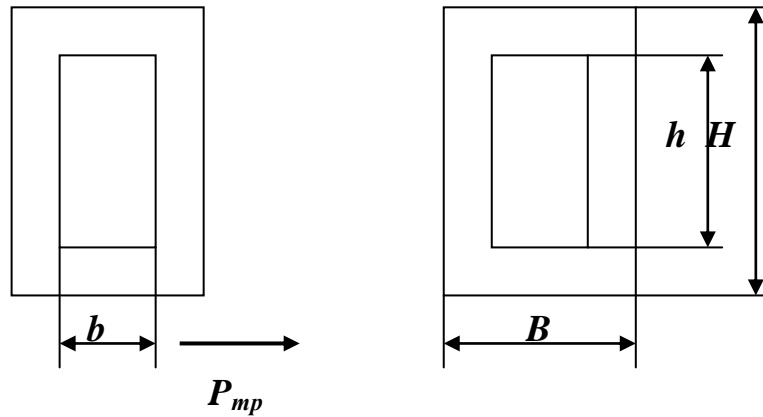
Розрахункова схема поперечного перерізу стійки коника
